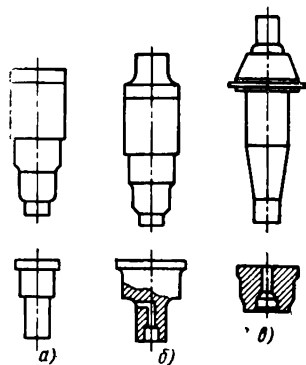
Варианты двухпереходной штамповки поковки ведущей шестерни: а — первый вариант первого перехода; б — второй вариант первого перехода; в — окончательная штамповка. Верхний ряд — переходы штамповки; нижний ряд — пуансоны
